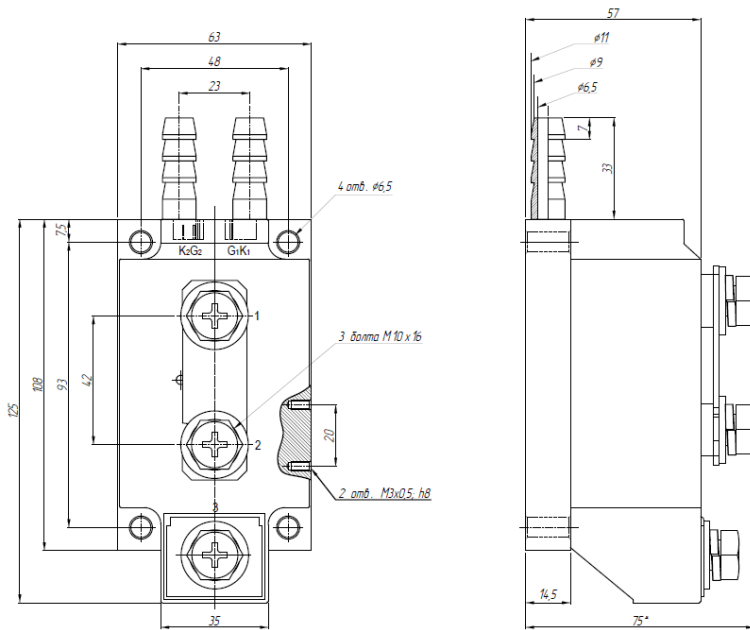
габаритные и установочные размеры ТТП серии GwDH-800120.ZD3
